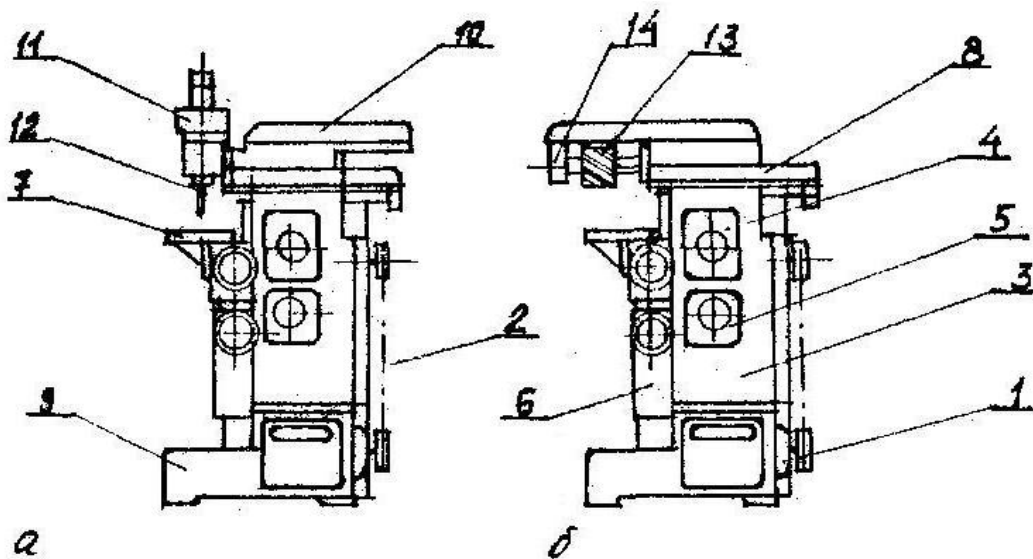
Основні вузли широкоуніверсального фрезерувального верстата
